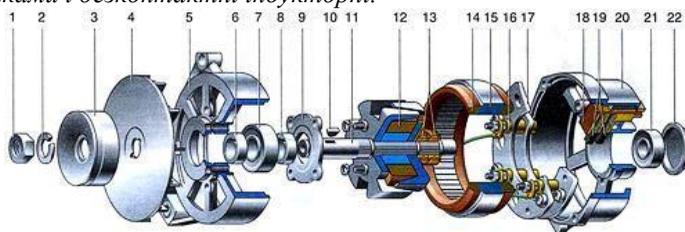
Генератор змінного струму: 1 - гайка шківів; 2 - шайба; 3 - шків; 4- крильчатка; 5 - передня кришка, 6, 8 - дистанційні втулки; 7- передній підшипник; 9- шайба; 10 - шпонка; 11 - вал ротора; 12 - ротор; 13 - контактні кільця; 14 - обмотка статора; 15 - статор; 16 - ізоляційна втулка діода випрямного блоку; 17 - пластина випрямного блоку; 18 - щітковий вузол; 19 - щітки; 20 - корпус регулятора напруги і щіткового вузла; 21 - задній підшипник; 22 - кришка заднього підшипника.
